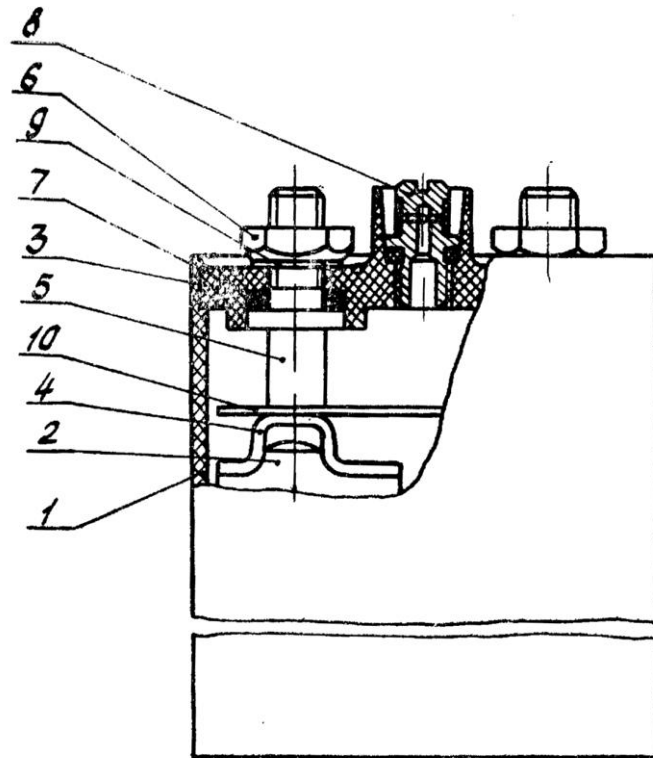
Лужний акумулятор (елемент) НКБН-25 1 - корпус; 2 - блок пластин (електродів); 3 - кришка; 4 - місток; 5 - Борн (полюсний штир); 6 - гайка; 7 - кільце ущільнювача; 8 - пробка; 9 - шайба; 10 - екран.
